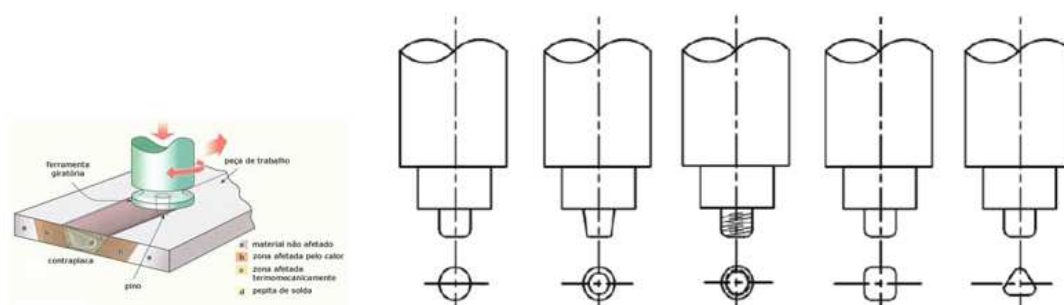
formatos das ferramentas para processo de soldagem por fricção. FONTE: New Trends In Welding In The Aeronautic Industry
